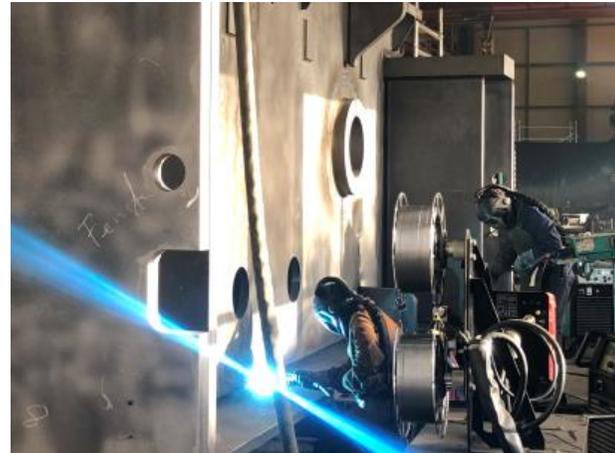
ANDRITZ Kaiser forderte bei den hunderten Metern Schweißnaht Champions League-Niveau bei der Schweißausführung.
